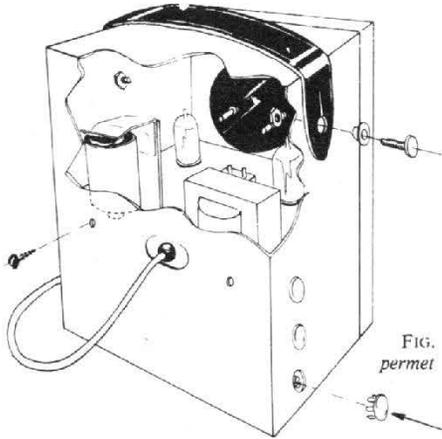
Vue arrière du 232, qui permet de voir la disposition interne des éléments.
